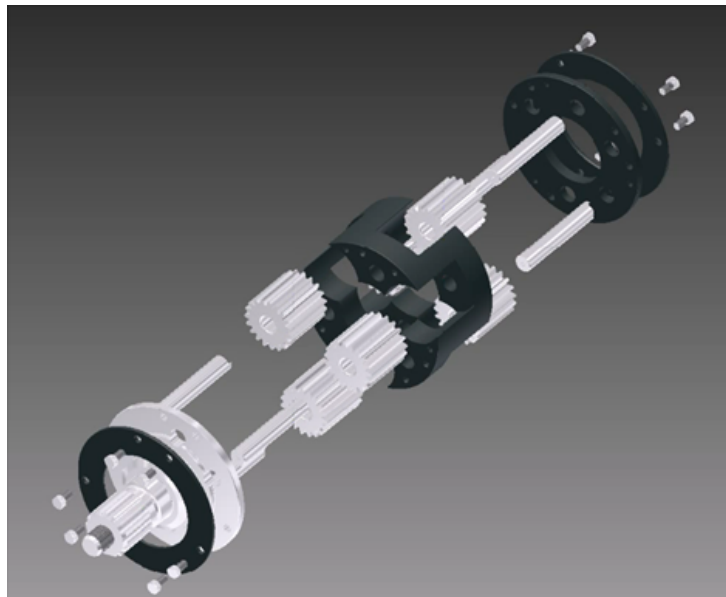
Планетарний механізм K2 із щепленими сателітами- збірка,рознесений вигляд.
